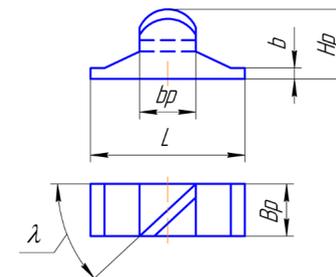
Конструкция вставного резца-зуба развёртки
